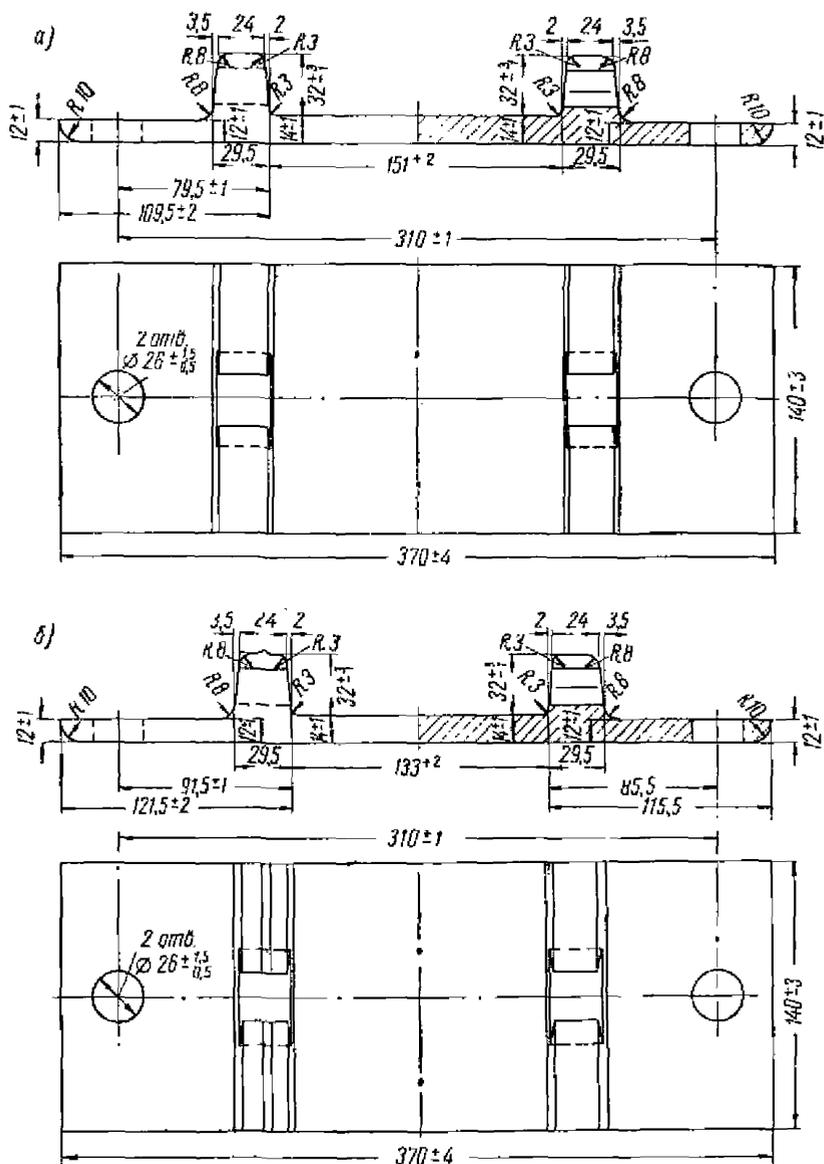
Подкладки марки К плоские с шурупным креплением к железобетонной шпале:
